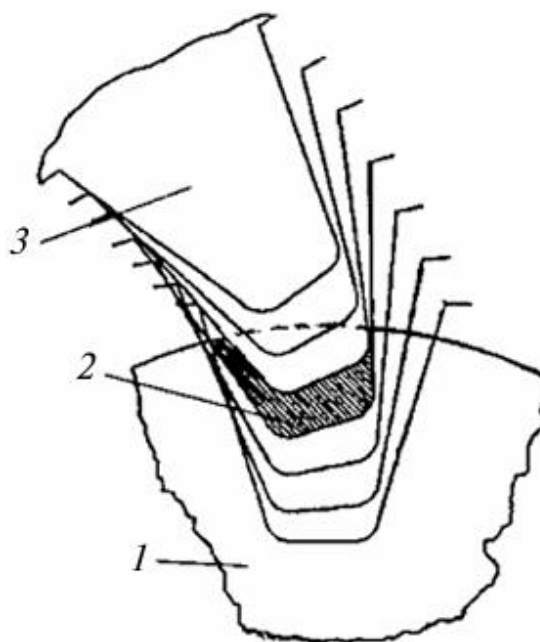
Схема нарезания зубьев червячной фрезой
